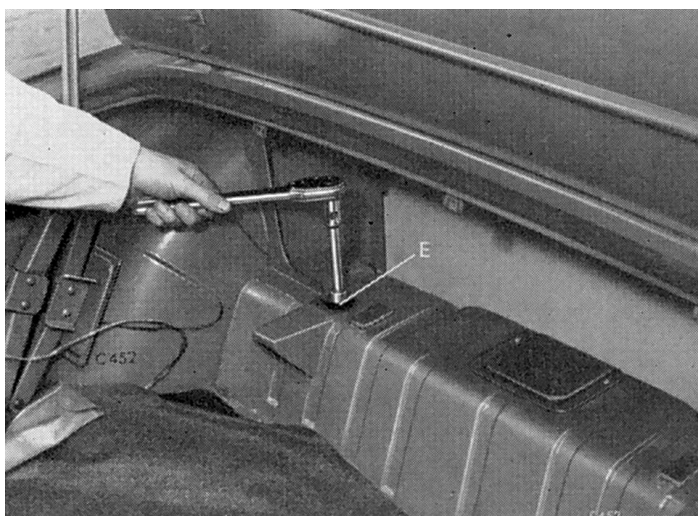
Points de fixation sur le tunnel de ressort de suspension
